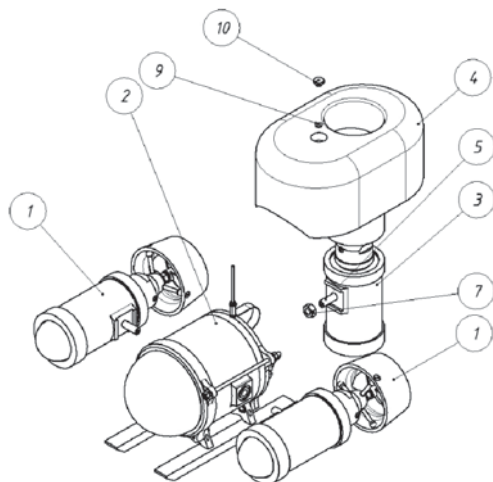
Схема сборки ТПА «ГНОМ BABУ»
